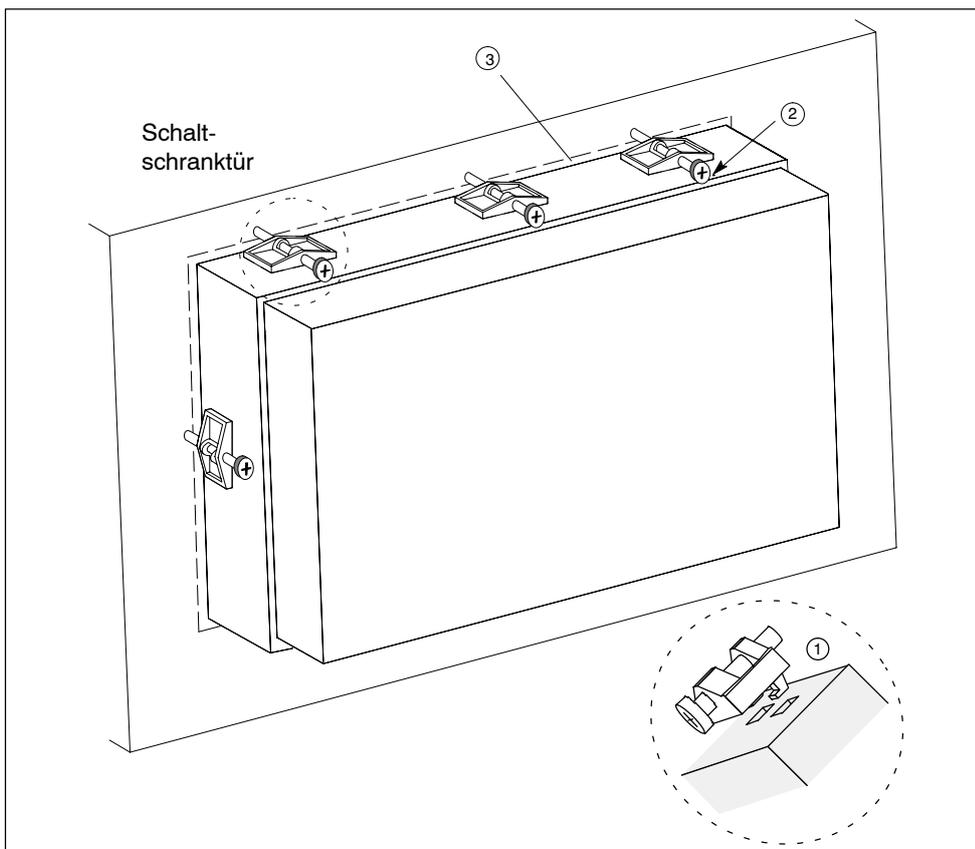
Mechanische Befestigung des C7-635 Touch
